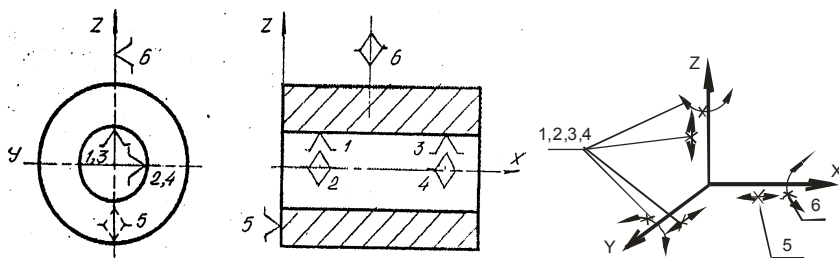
Теоретическая схема базирования заготовки по плоскости и внутренней цилиндрической поверхности (по длинному цилиндрическому отверстию)
